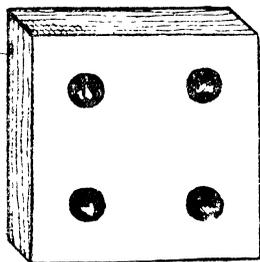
Двойная (квадратная) планка с 4 дырочками.
